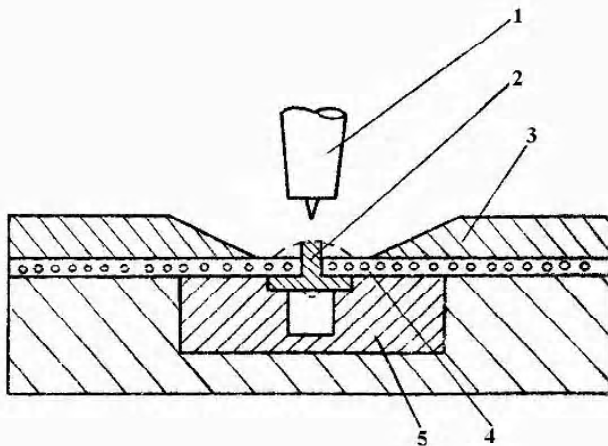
Схема зварювання листового КМ ВКА-2 через проміжкову Т-подібну вставку, яка розплавляється:
